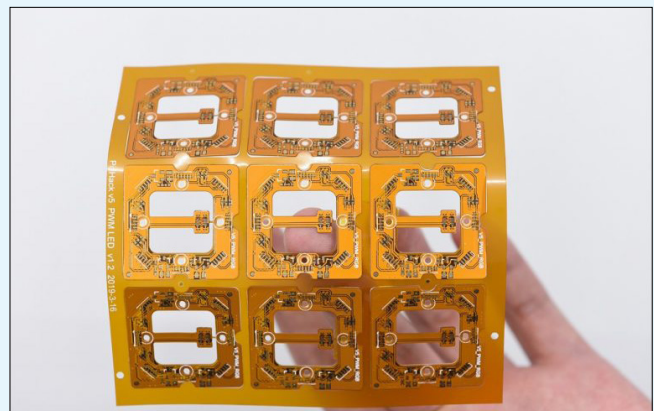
Esempio di PCB Rigid-Flex (fonte: [www.pcbway.com](http://www.pcbway.com))
